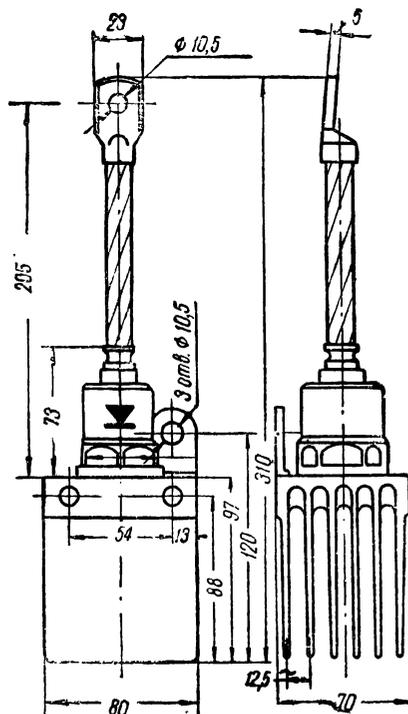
Габаритные размеры кремниевого вентиля ВК-200
